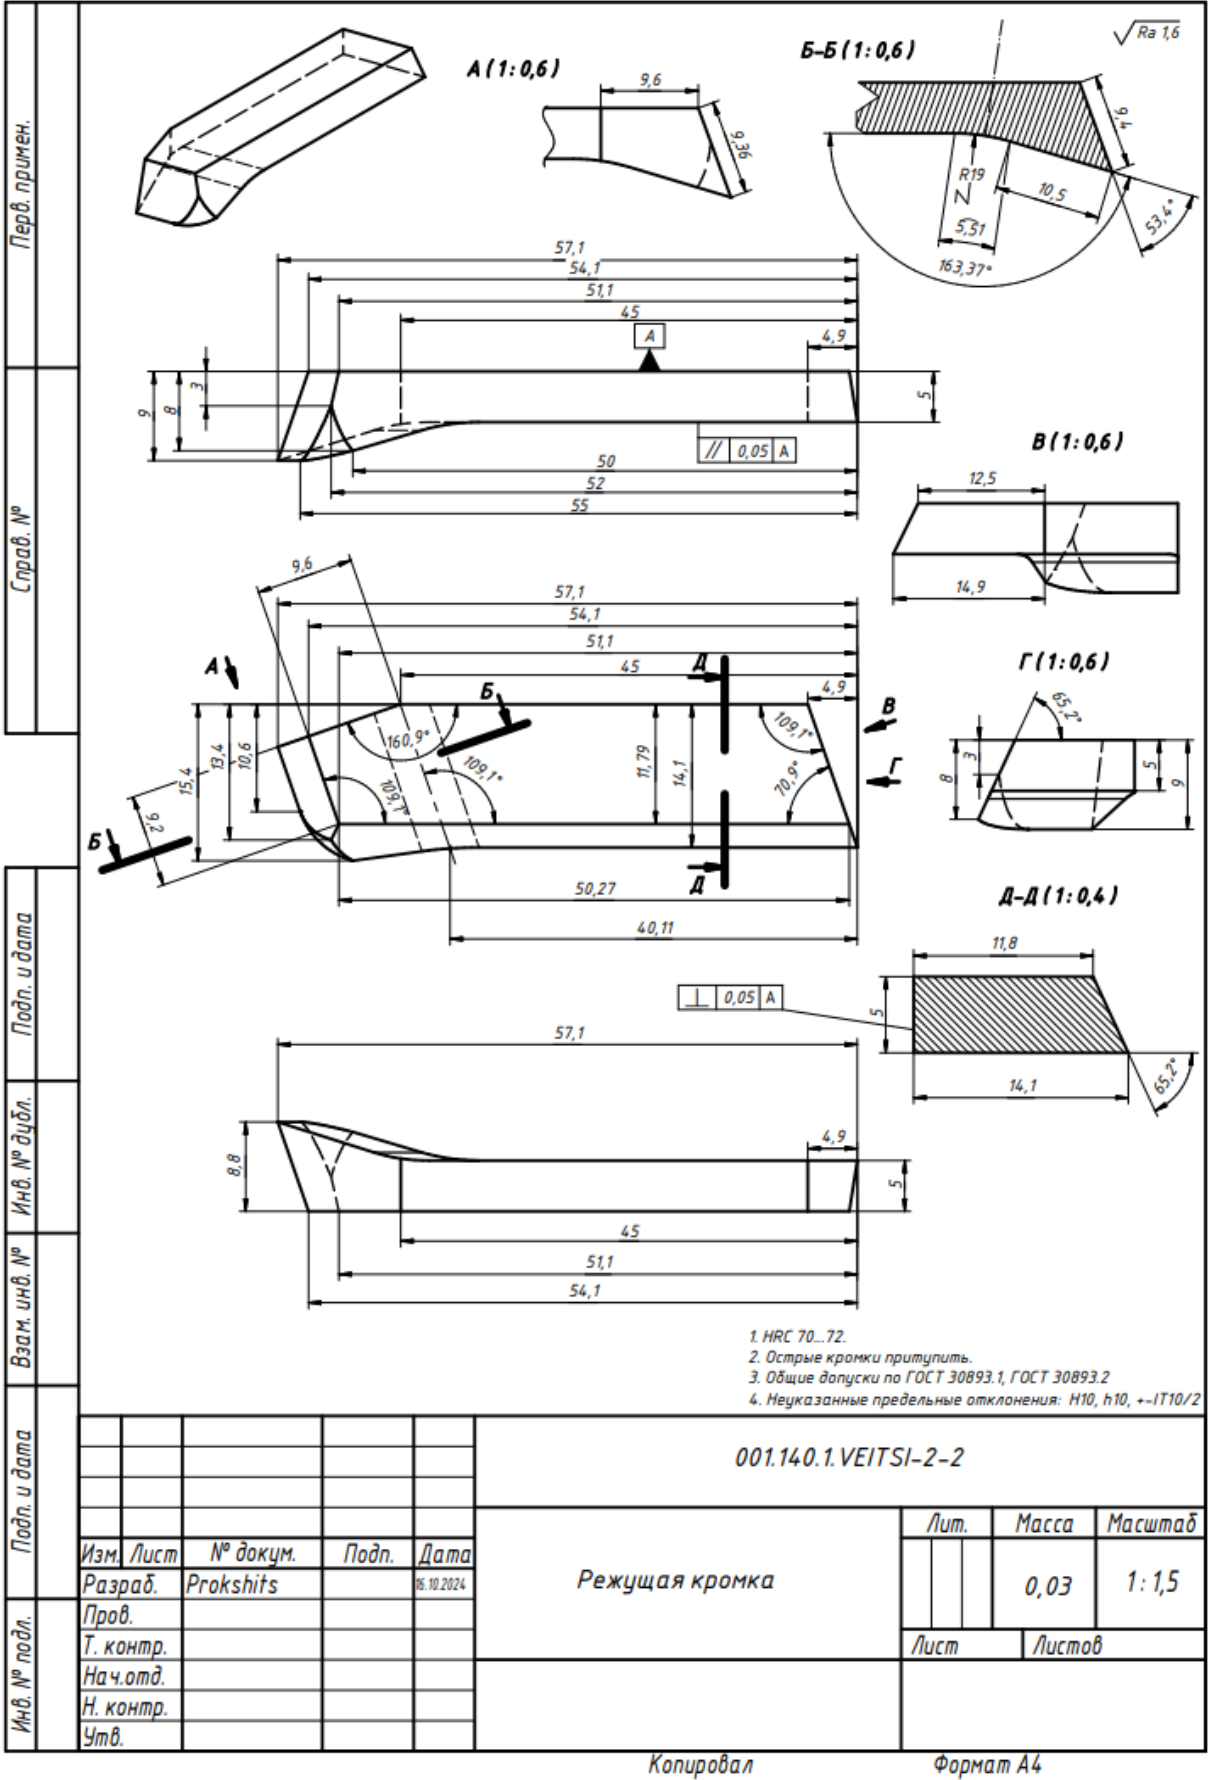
Чертеж режущей кромки сменного лезвия короснимателя
